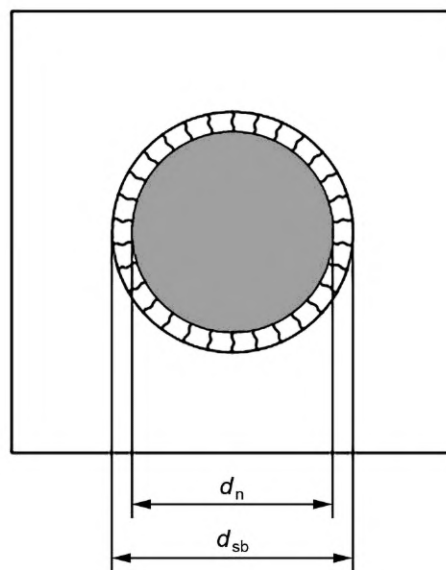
Измерения диаметра при сварке листов с металлическим покрытием с областью пайки
